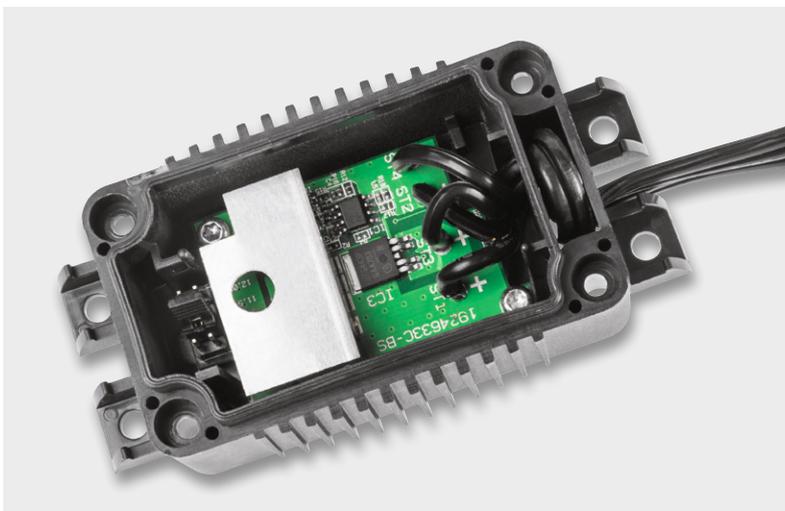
Einbau und Verschrauben der Platine im Gehäuseunterteil
